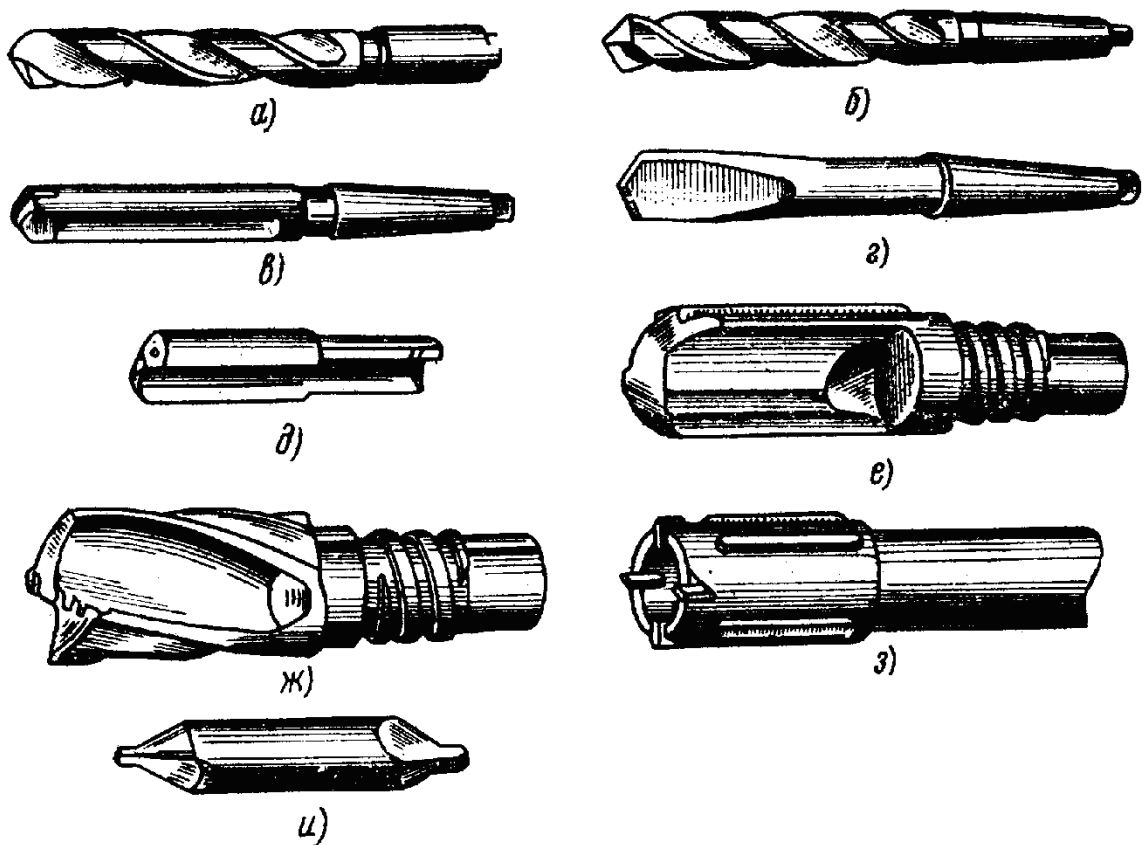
Некоторые типы свёрл: а, б - спиральное; в - с прямыми канавками; г - перовое; д - ружейное; е - однокромочное с внутренним отводом стружки для глубокого сверления; ж - двухкромочное для глубокого сверления; з - кольцевое; и - центровочное.
